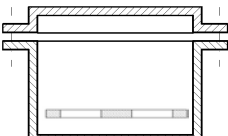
Explosionsdruckfeste Gehäusegeometrien
